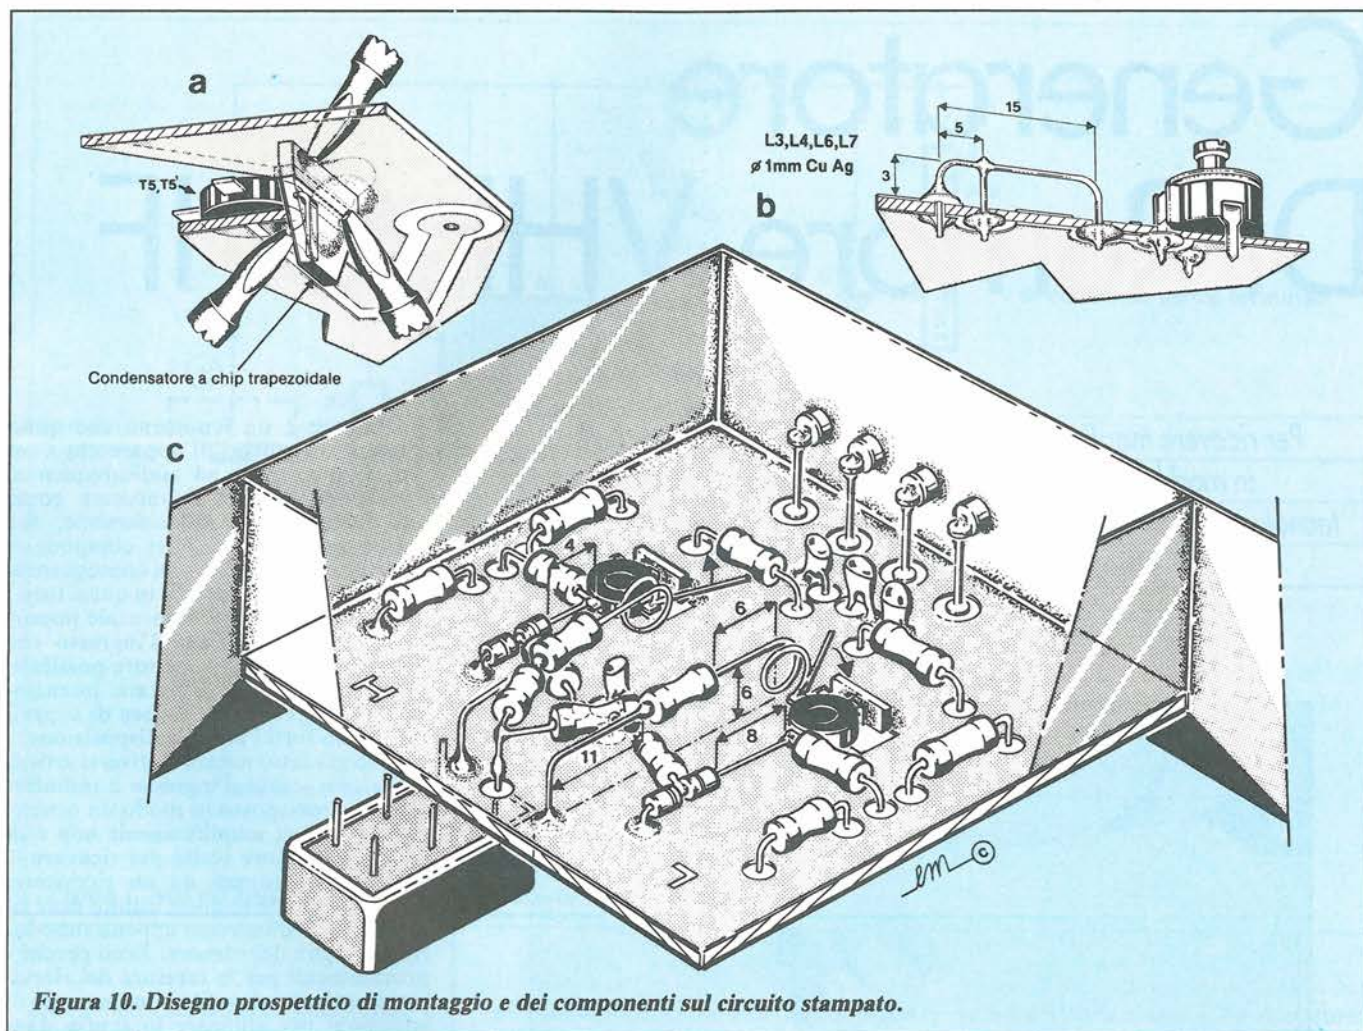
Disegno prospettico di montaggio e dei componenti sul circuito stampato.
